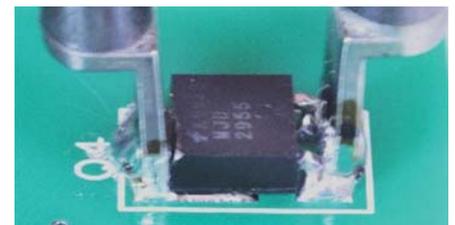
Confirmar la Fusión de la Soldadura y Levantar el Componente.
